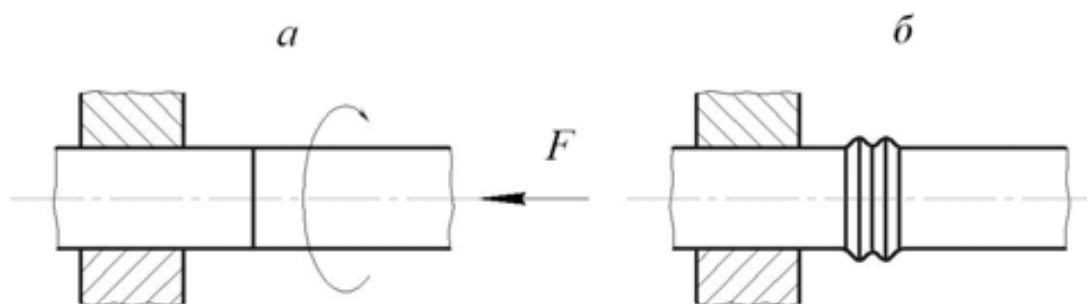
Принципиальная схема сварки трением: *а* – перед началом сварки; *б* – в конце сварки
